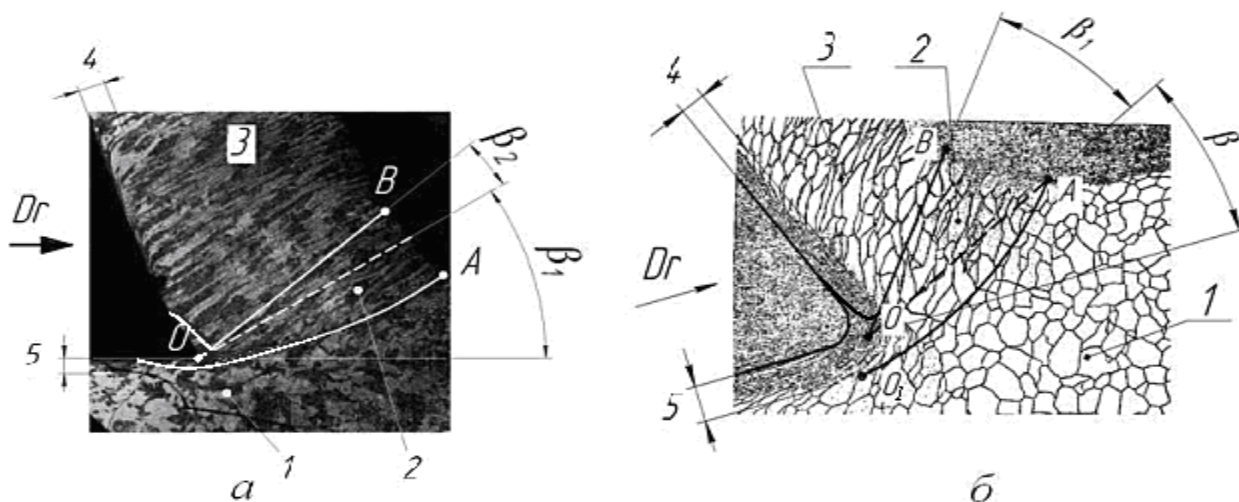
Стружкоутворення під час різання: а) сталі 30Х; б) жароміцного сплаву ХН77ТЮР: 1 – вихідна структура; 2 – зона стружкоутворення; 3 – стружка; 4 – зона вторинної деформації стружки; 5 – деформований шар обробленої поверхні заготовки
